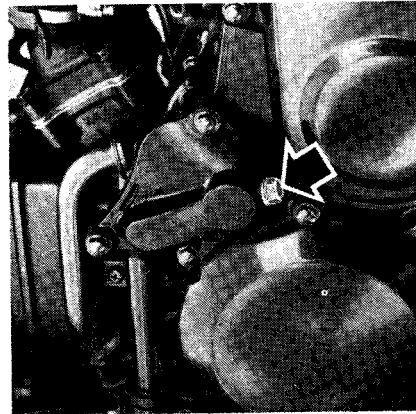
Vis de vidange du circuit de refroidissement sur la pompe à eau (Photo RMT)
